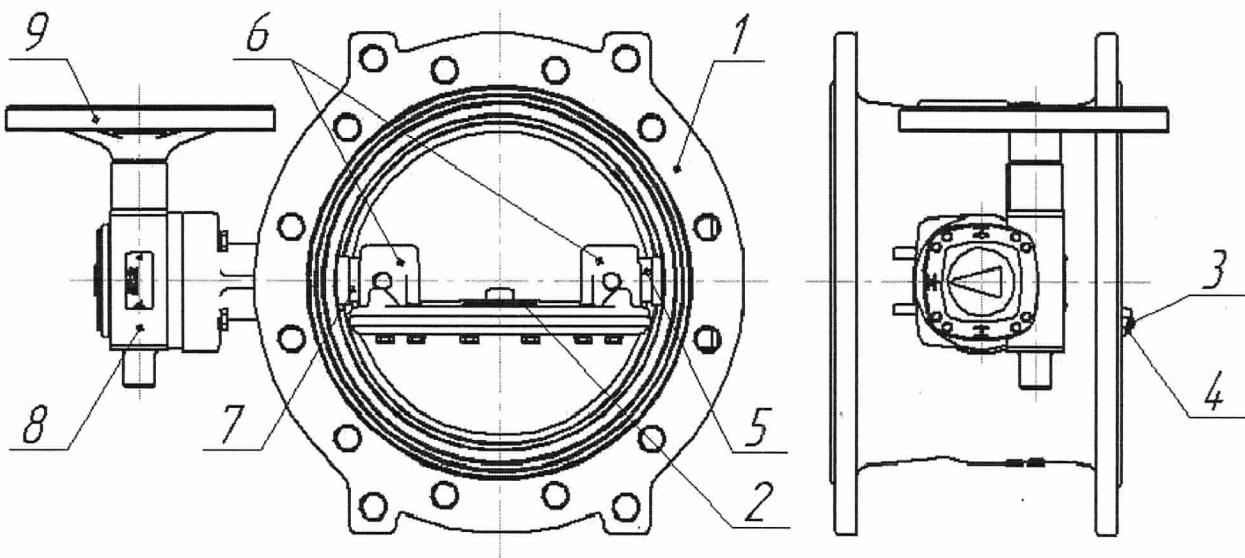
Устройство затвора с ручным приводом и штурвалом
